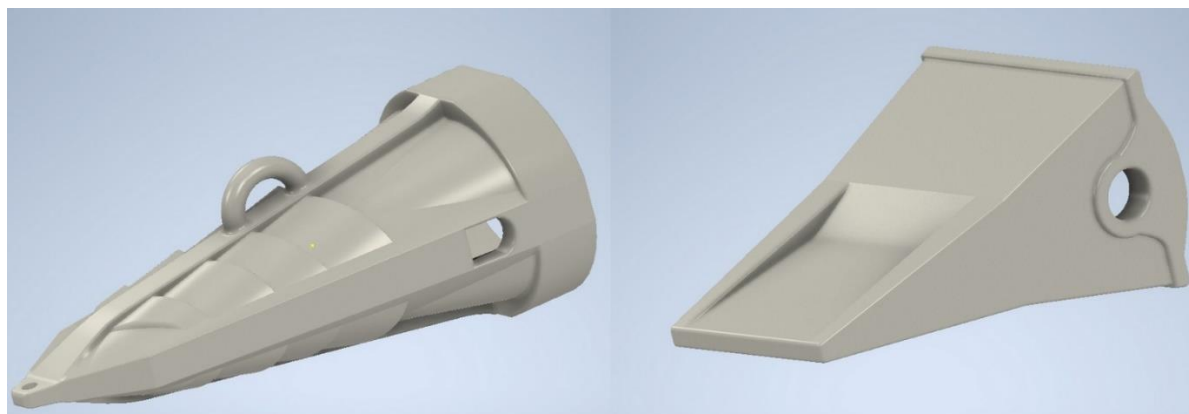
Коронки для адаптеров ковшей экскаватора
